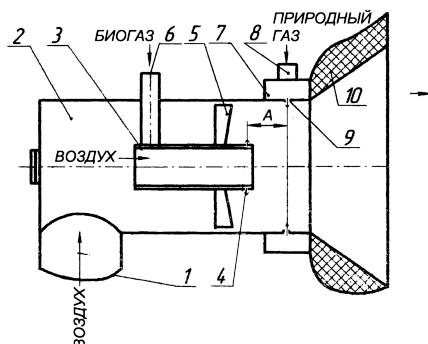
Двухколлекторная горелка: 1 – воздухопровод; 2 – корпус горелки; 3 – кольцевой коллектор; 4 – сопла для биогаза или газа; 5 – лопаточный завихритель дутьевого воздуха; 6 – патрубок подачи биогаза или газа; 7 – кольцевая газовая камера; 8 – патрубок для подачи газа; 9 – газовые сопла; 10 – амбразура.
